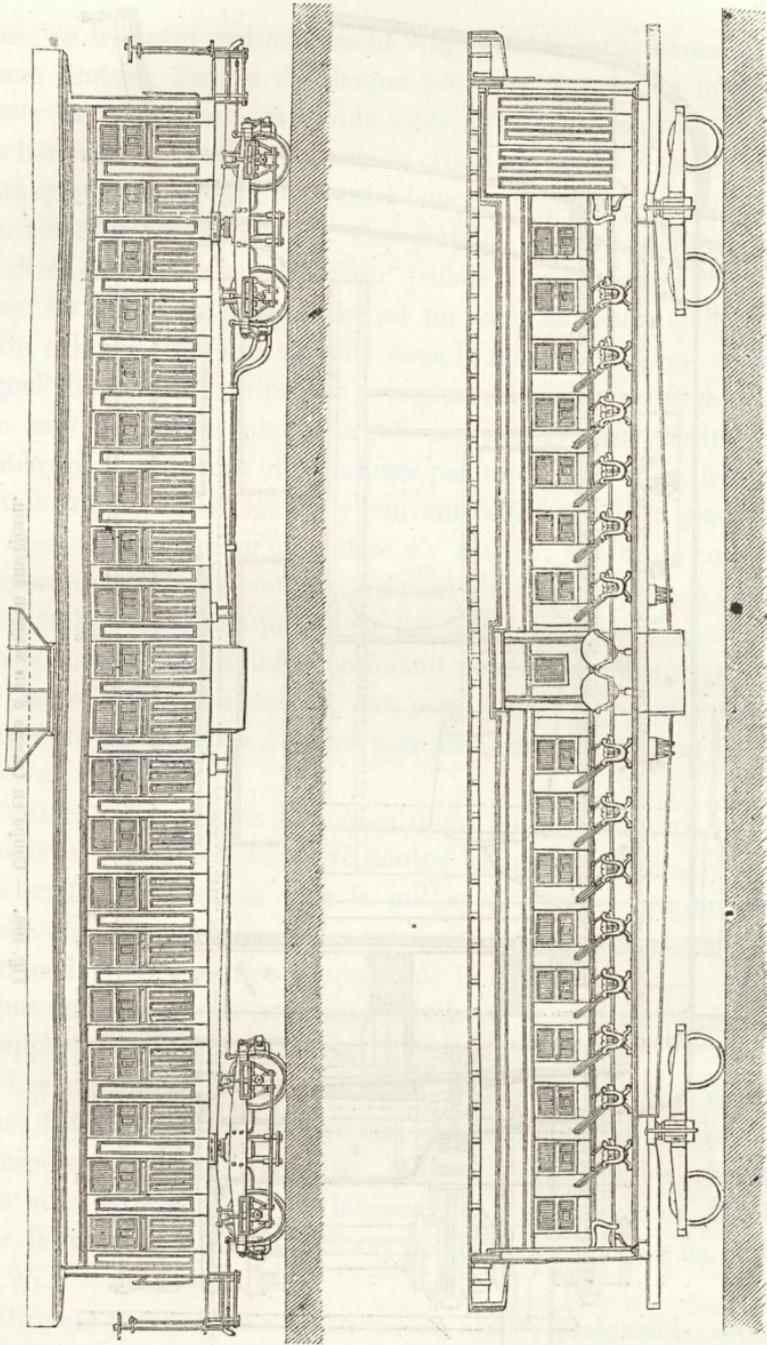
Élévation et coupe longitudinale d'un waggon américain.
